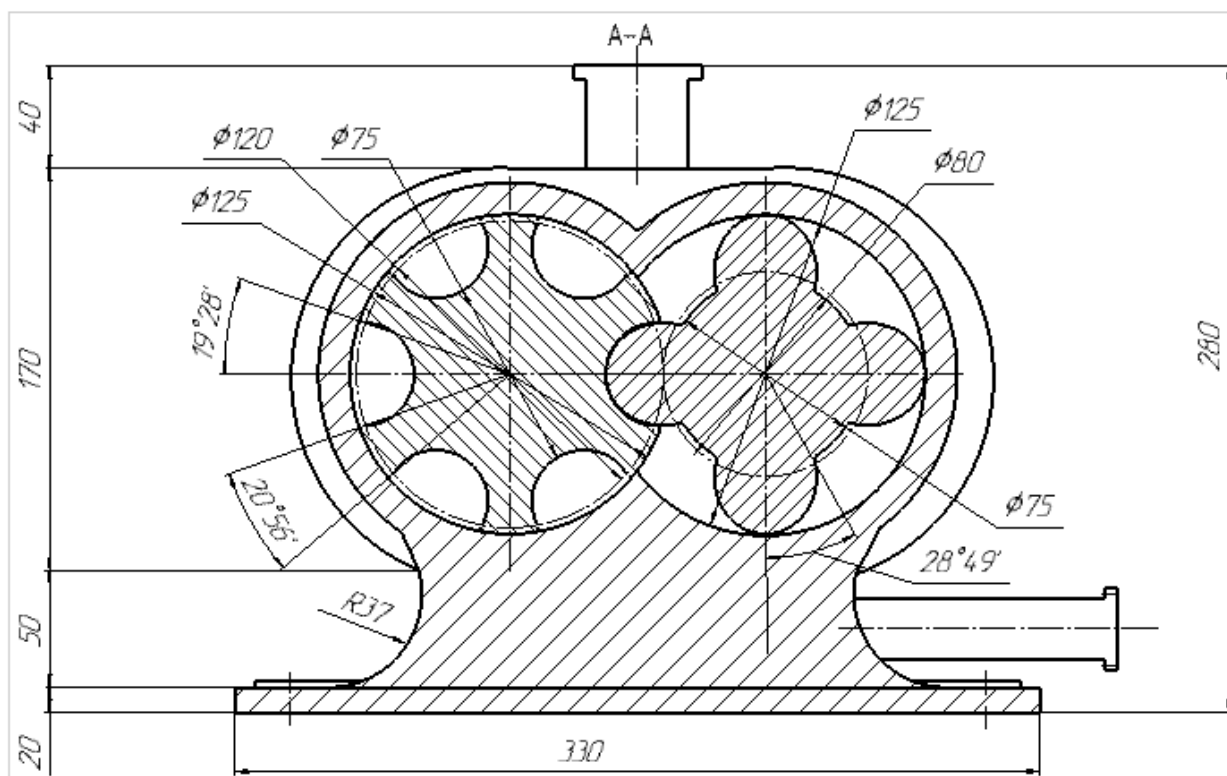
Поперечный разрез винтового компрессора 2 ступени.
